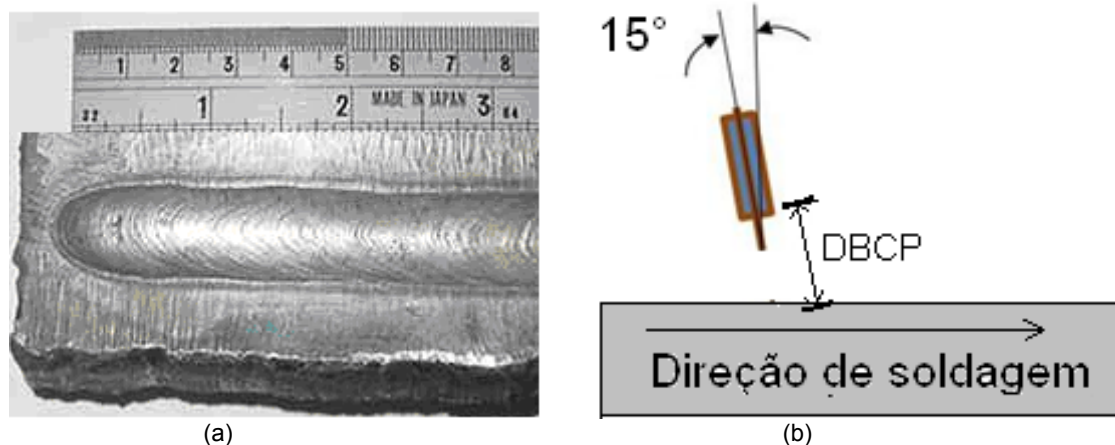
(a) Imagem do cordão de solda e (b) Técnica e procedimentos de soldagem.
